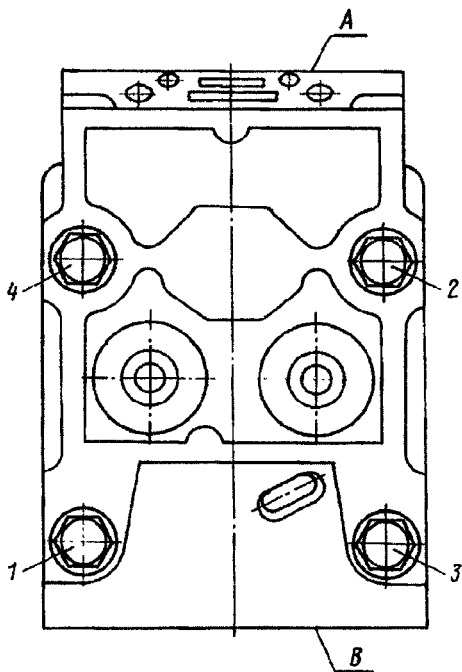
Схема затяжки болтов крепления головки цилиндра:
